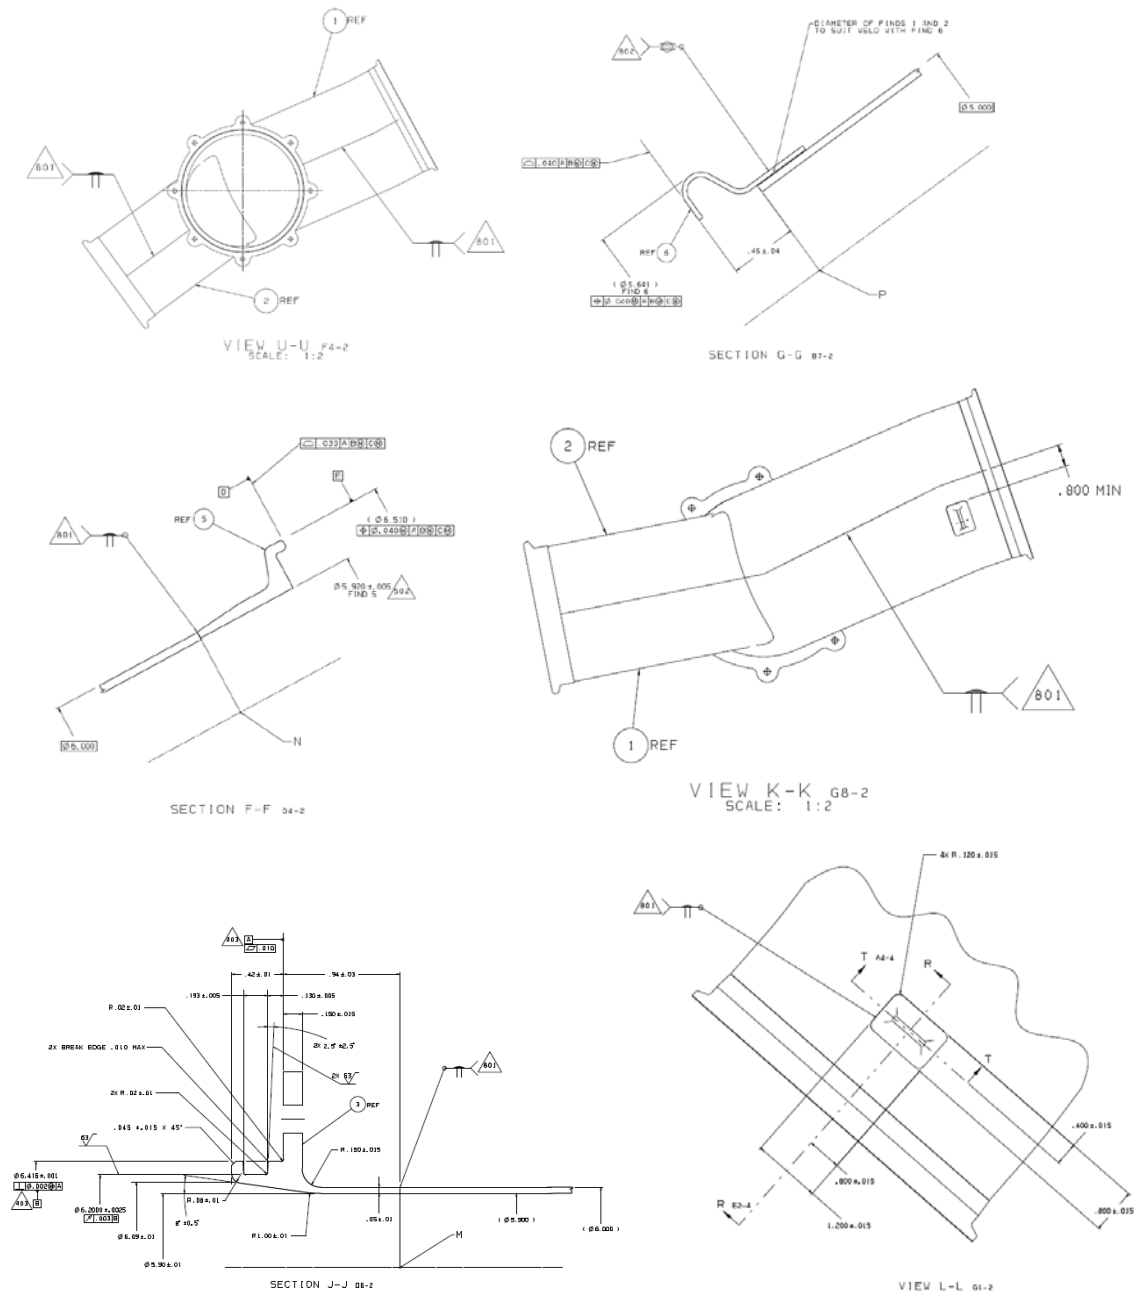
Puntos de soldadura del Bleed Duct (Honeywell International Inc., 2009).
